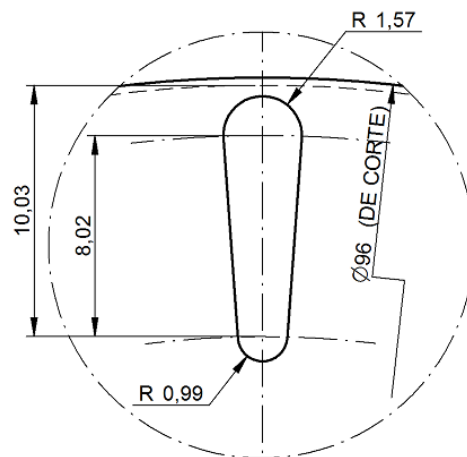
Desenho com as dimensões da ranhura do rotor da máquina de indução original.
